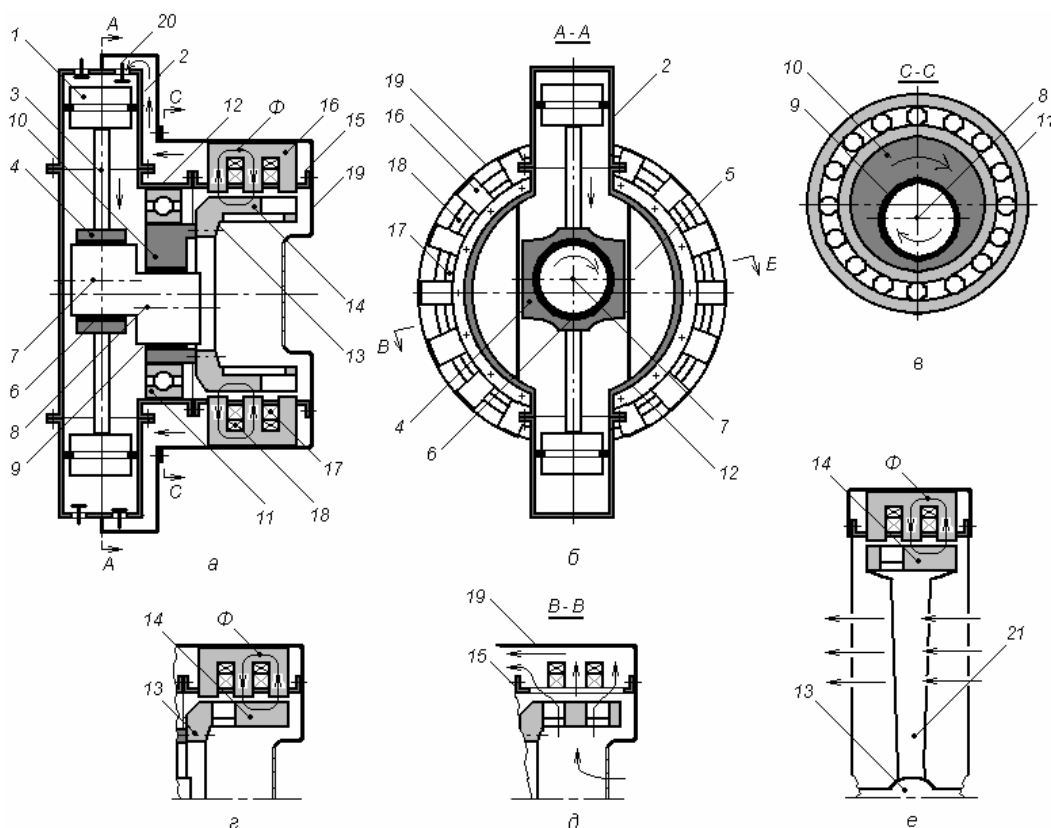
Эксцентриковый поршневой ДВС с модульным индукторным генератором: а – продольный разрез агрегата; б – поперечный разрез; с – эксцентриковый вал в подшипнике; д – модуль генератора с приводом от ДВС; е – вентиляция обмоток генератора; ф – модуль генератора с приводом от турбины
